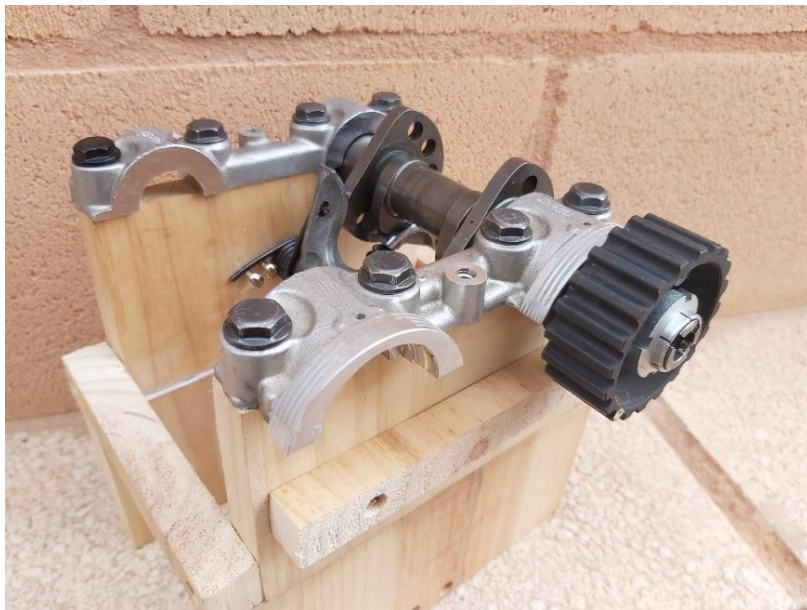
Vista perfil 1 de la maqueta finalizada. Fuente: Propia
